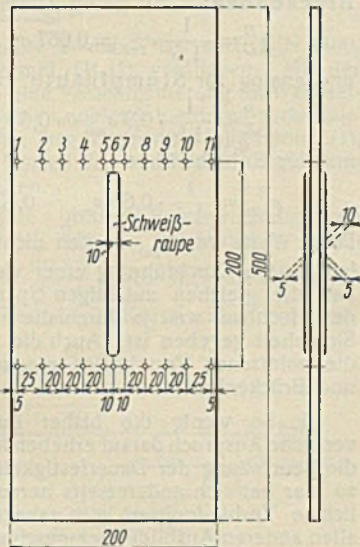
Probestab für die Messung der Schrumpfungen beim Lichtbogenschweißen.
